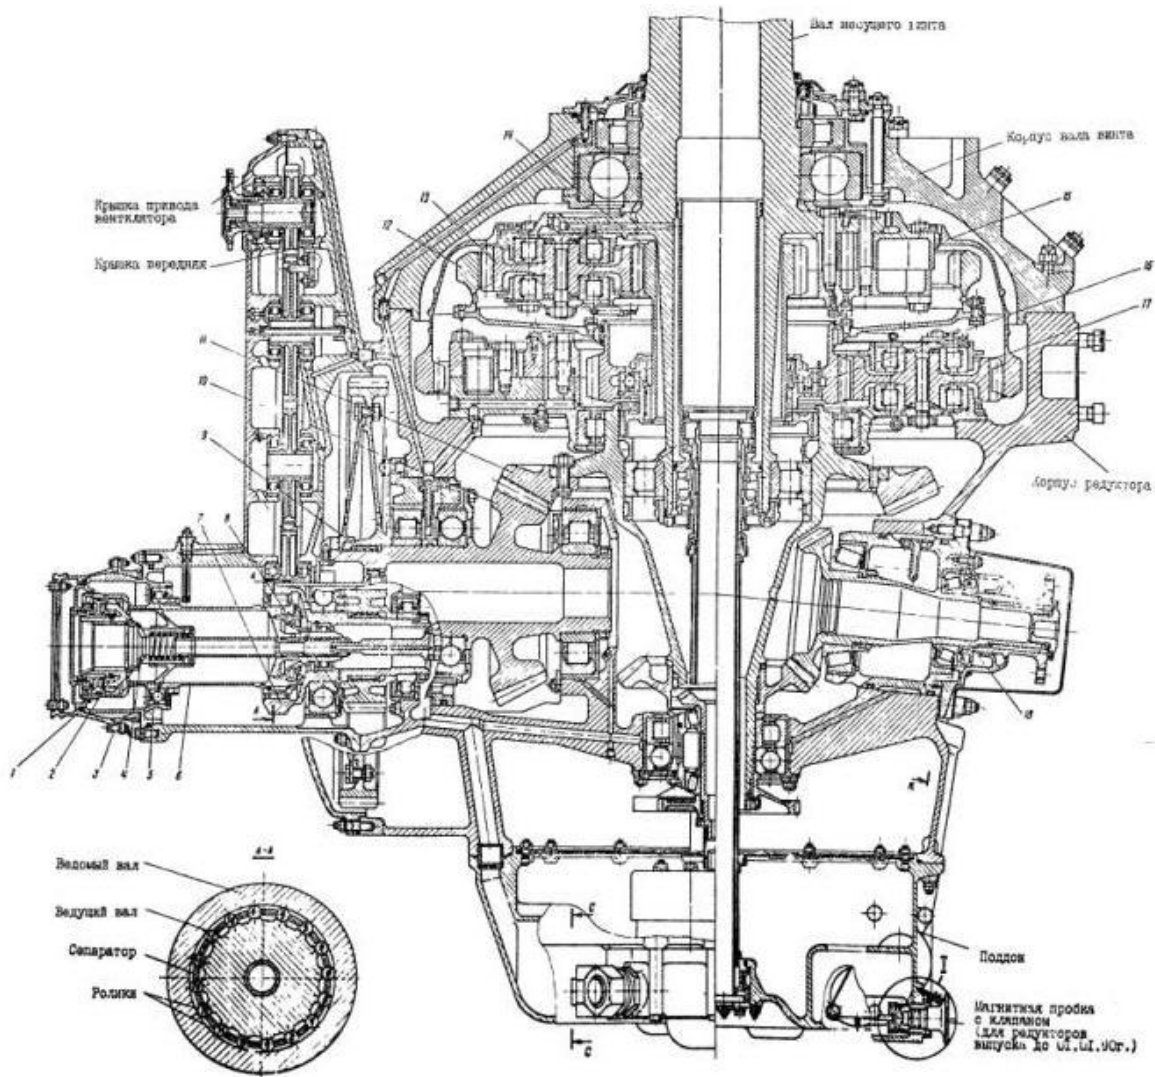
Поздовжній розріз головного редуктора ВР-14:
